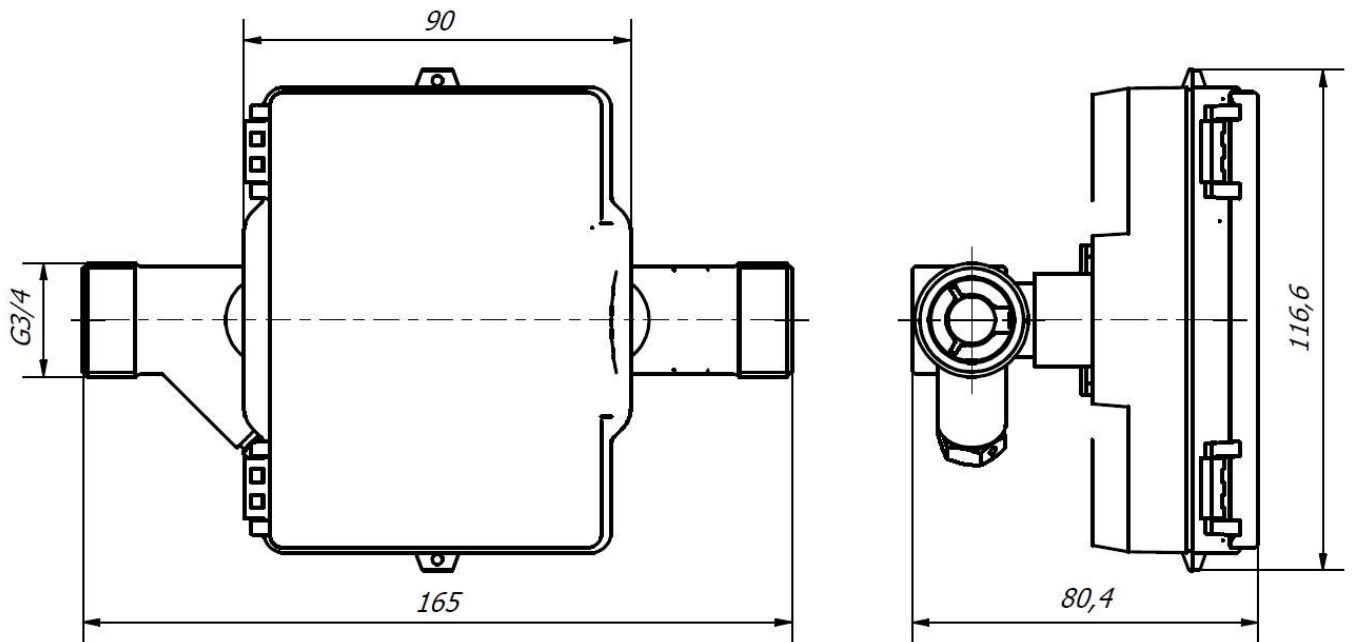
Gjengede endetilkoblinger G3/4", monteringslengde L=165 mm.
